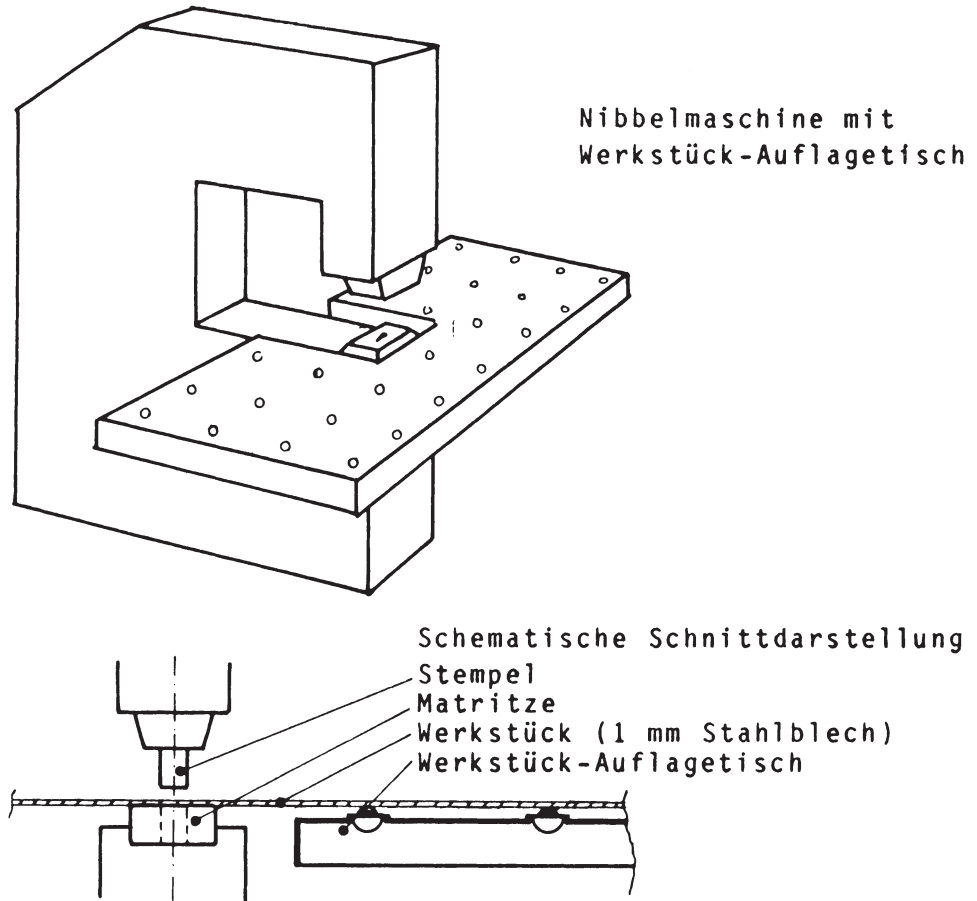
Nibbelmaschine mit Werkstück-Auflagetisch.
